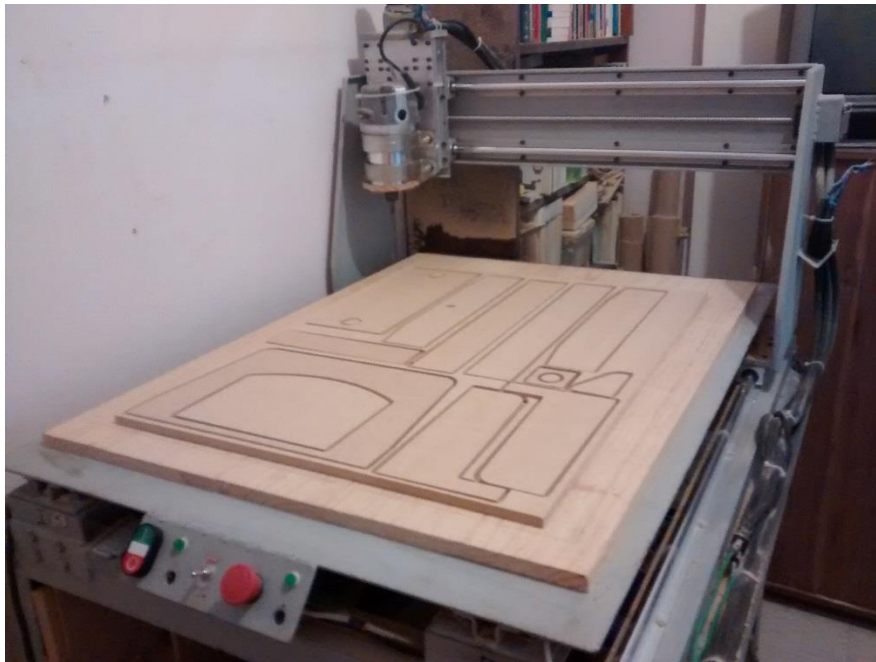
Máquina CNC utilizada para la fabricación de las piezas estructurales del prototipo de la Bio-impresora 3D.
